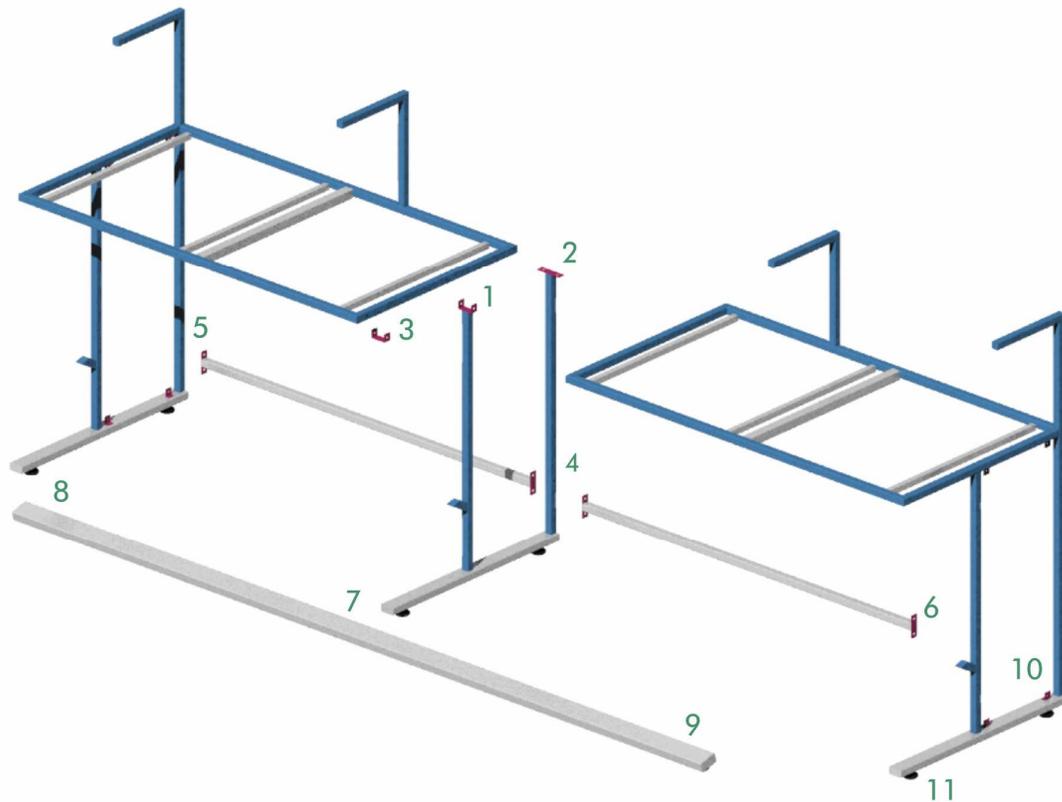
Elementos en que se divide la estructura de la mesa de trabajo.
